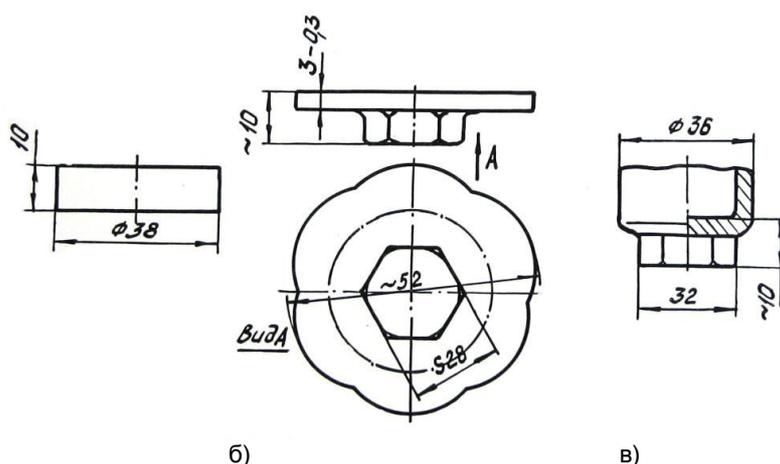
Технология холодной объемной штамповки крышки гидросистемы: а – исходная заготовка; б – контурная осадка заготовки на матрице с шестигранным отверстием; в – операция вытяжки-свертки
